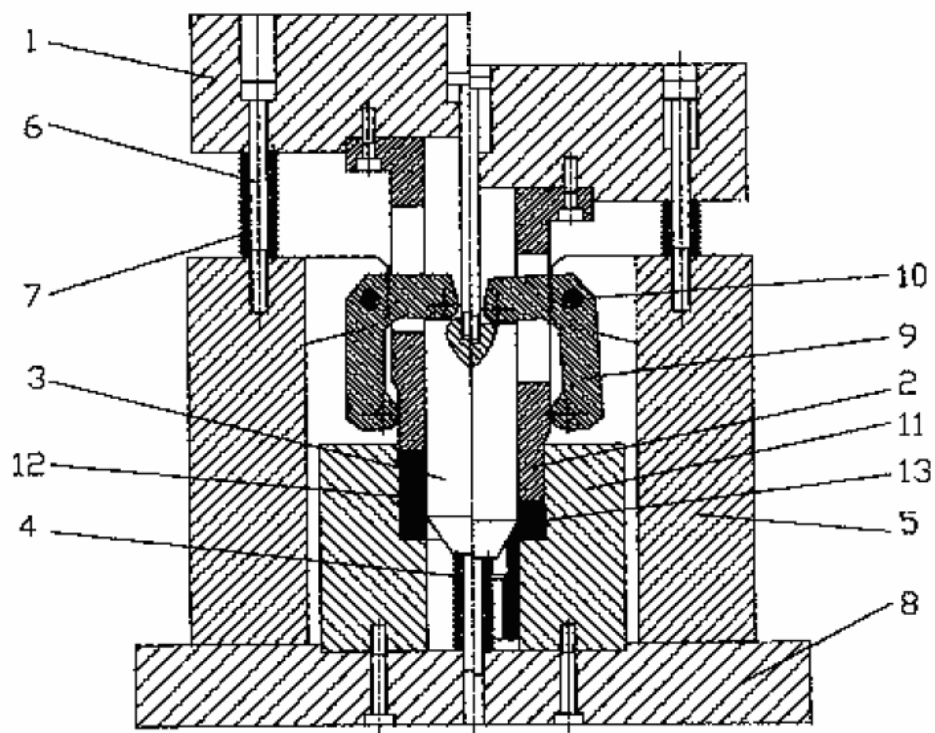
Штамп для видавлювання порожнистих деталей зі складним профілем
